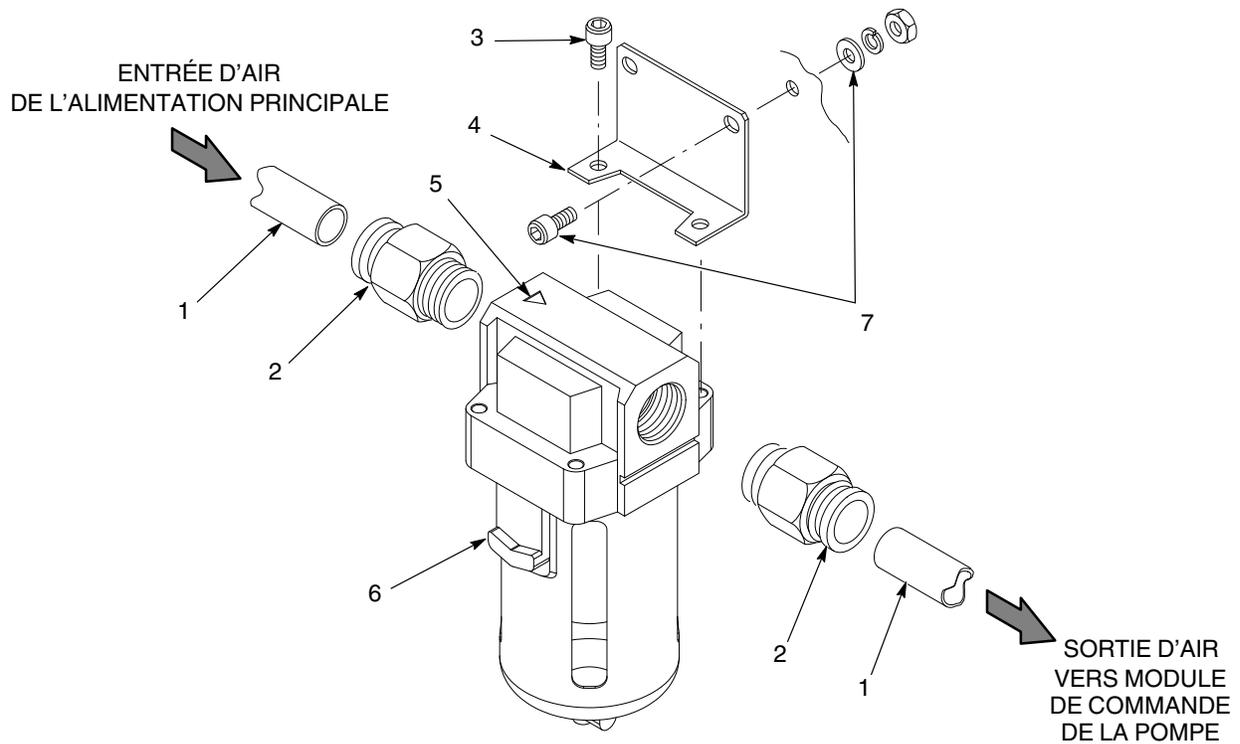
Installation du filtre à air – Systèmes autonomes et à montage mural/sur rail
